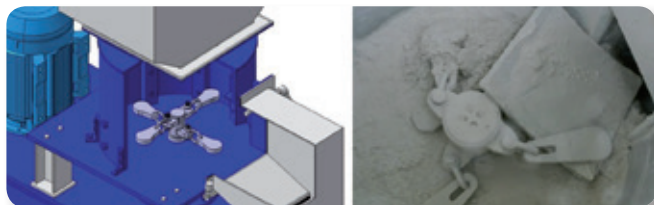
Diseño y disposición martillos (izquierda), martillos reales colocados en el molino (derecha). | Figure 4. Design and arrangement of hammers (left), real hammers fitted to the hammer mill (right).
